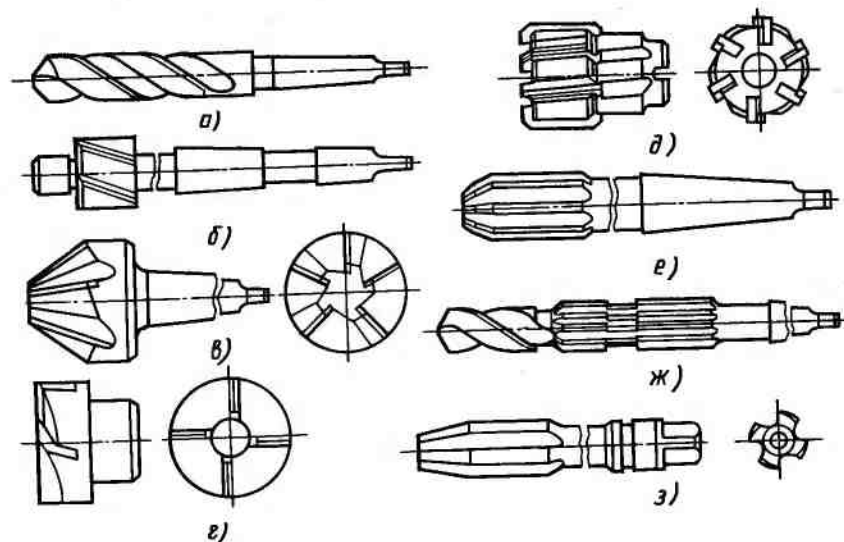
Режущие инструменты для обработки отверстий на сверлильных станках
